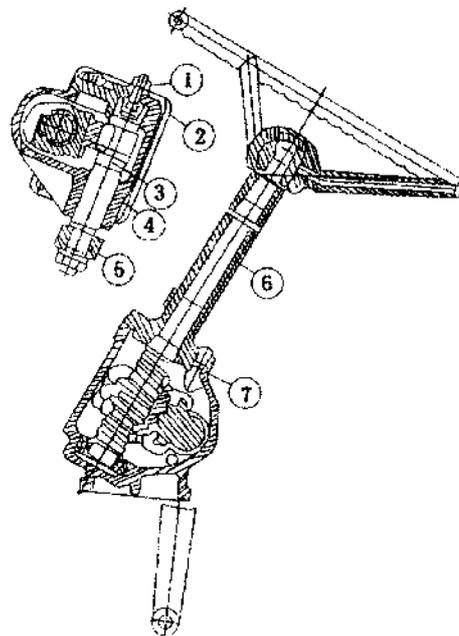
12. Рулевой механизм – шарьковая гайка – рейка – сектор
